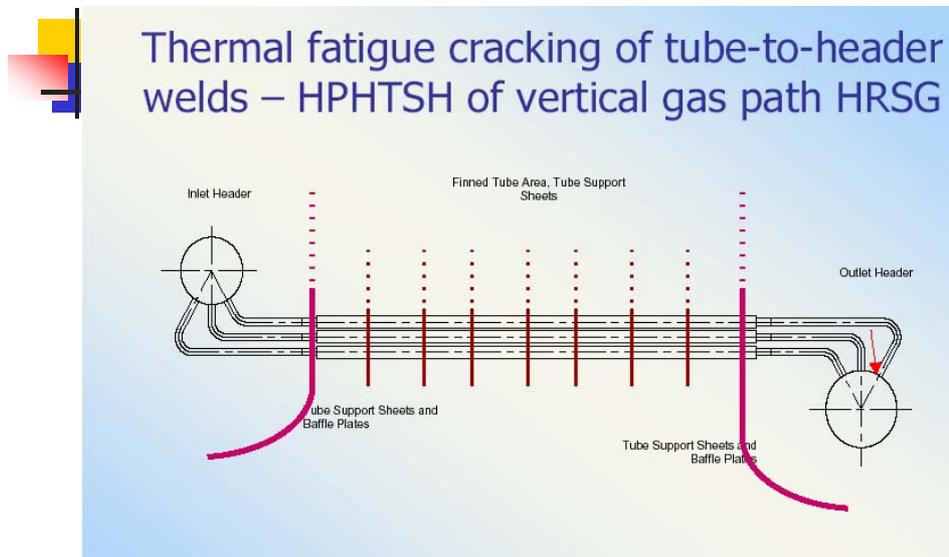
熱回收鍋爐之典型熱疲勞裂縫發生於燃氣側之集管與短管焊接地方
